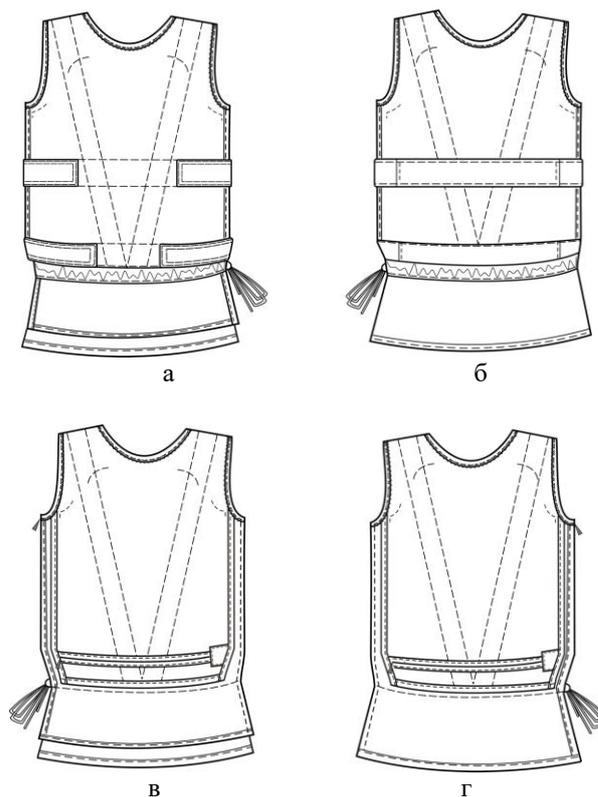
Эскиз модели бронезилета скрытого ношения: а) внешний вид переда; б) внешний вид спинки; в) внутренний вид переда; г) внутренний вид спинки
